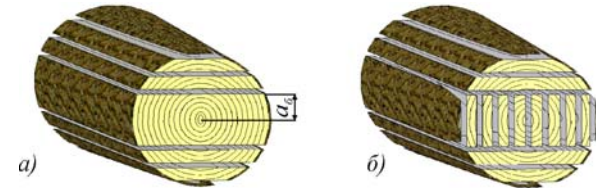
Схема розпилювання колод брусо-розвальним способом з формою поперечного перетину у вигляді еліпса:
